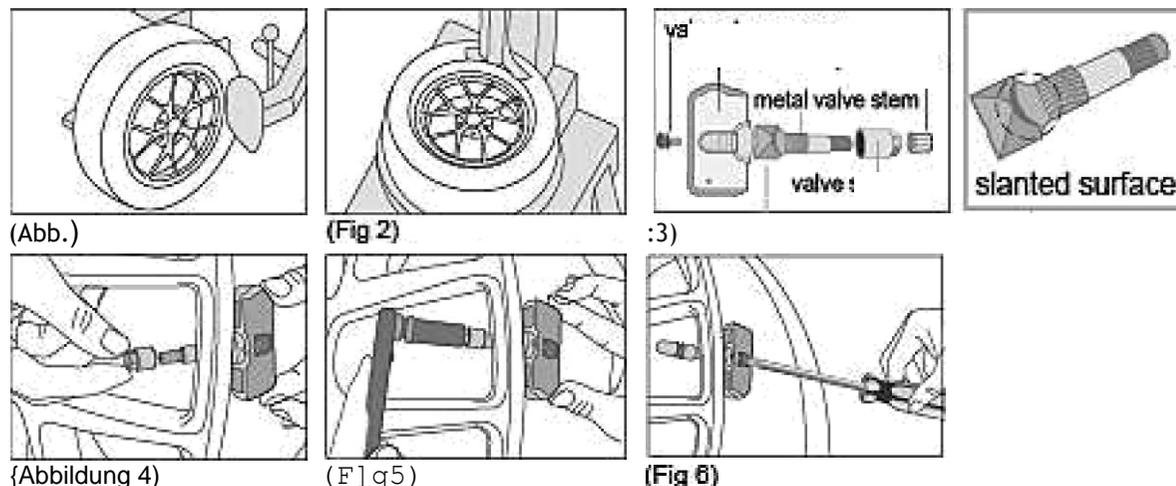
Halten Sie den Sensor in Position und führen Sie die Unterlegscheibe auf den Metallventilschaft an der Außenseite des Felgenlochs. Befestigen Sie dann die Ventilschaftmutter auf dem Metallventilschaft und ziehen Sie sie mit einem Drehmoment von 4 N-m (2,95 Ft-lbs) an. *Bringen Sie dann die Kunststoffkappe auf dem Metallventilschaft an.
